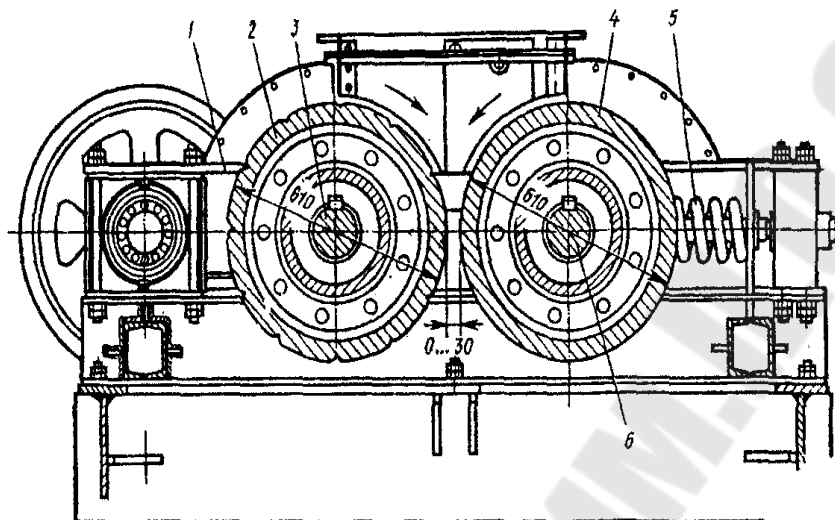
Общий вид валковой дробилки: 1- станина; 2,4- параллельные цилиндрические валки, вращающиеся на встречу друг другу; 3,6- подшипники; 5- пружинная опора
